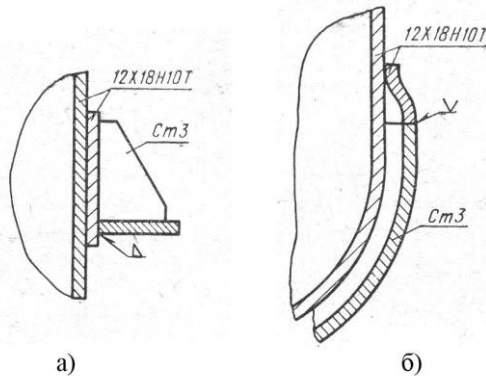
Конструктивное оформление сварных узлов деталей из разнородных сталей с использованием промежуточного элемента из высоколегированной стали: а) крепление лапы; б) крепление рубашки
